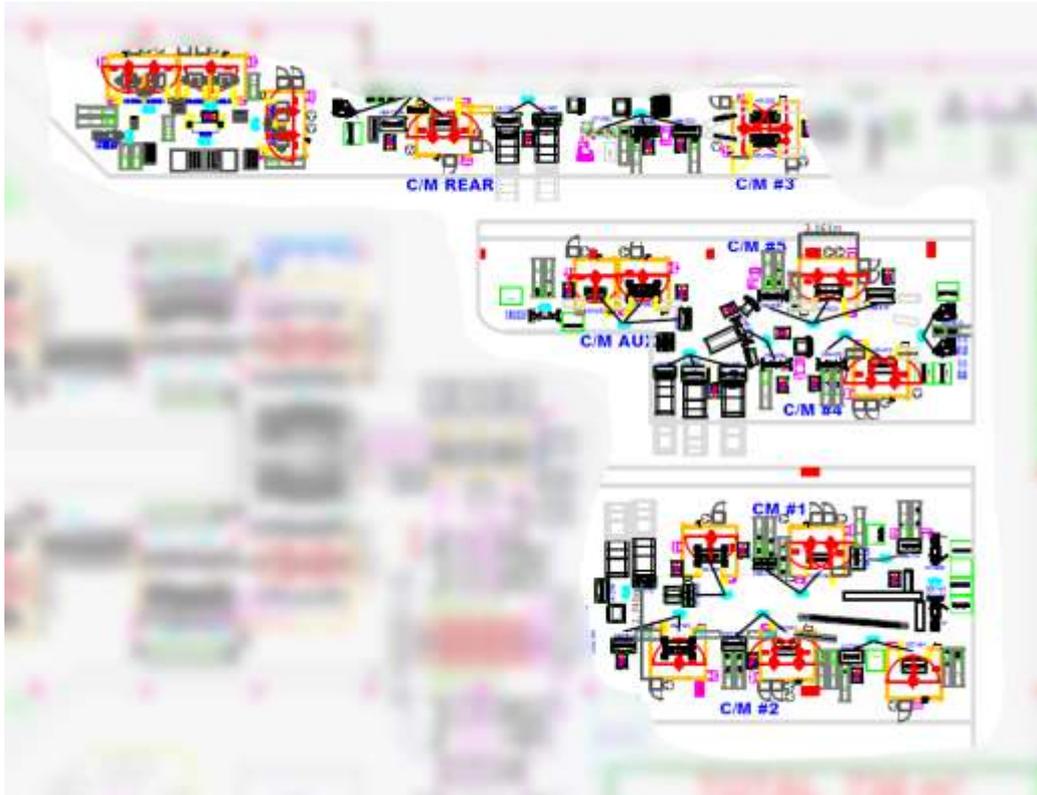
Layout de la soldadura de Cross Member para Toyota. Provisto por Metalsa.
